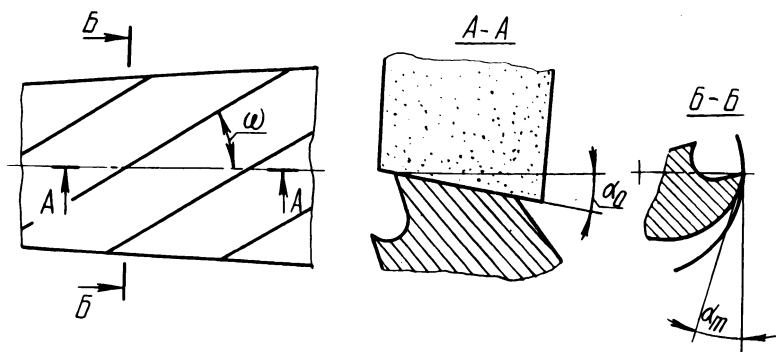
Схема затачивания зуба силовой развертки по прямой образующей.
